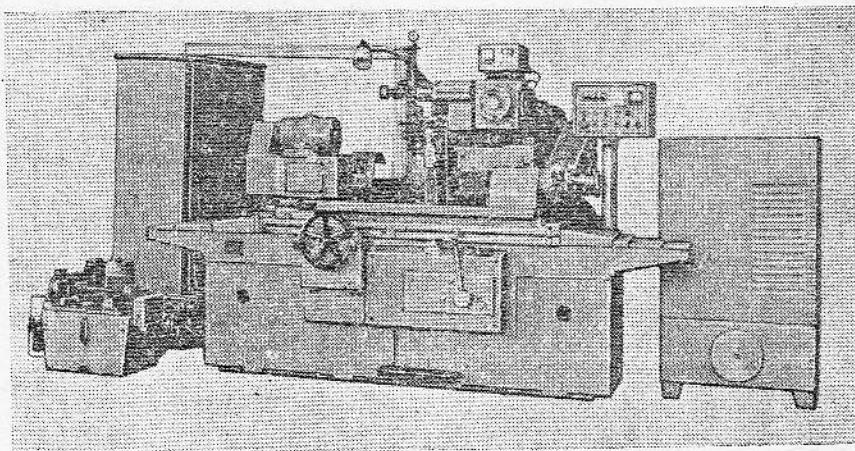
Станок круглошлифовальный универсальный ЗУ131ВМ
